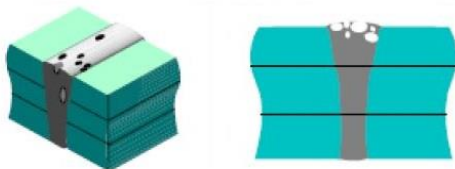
Schweißnahtfehler „Pore“ als Porennest [6]
